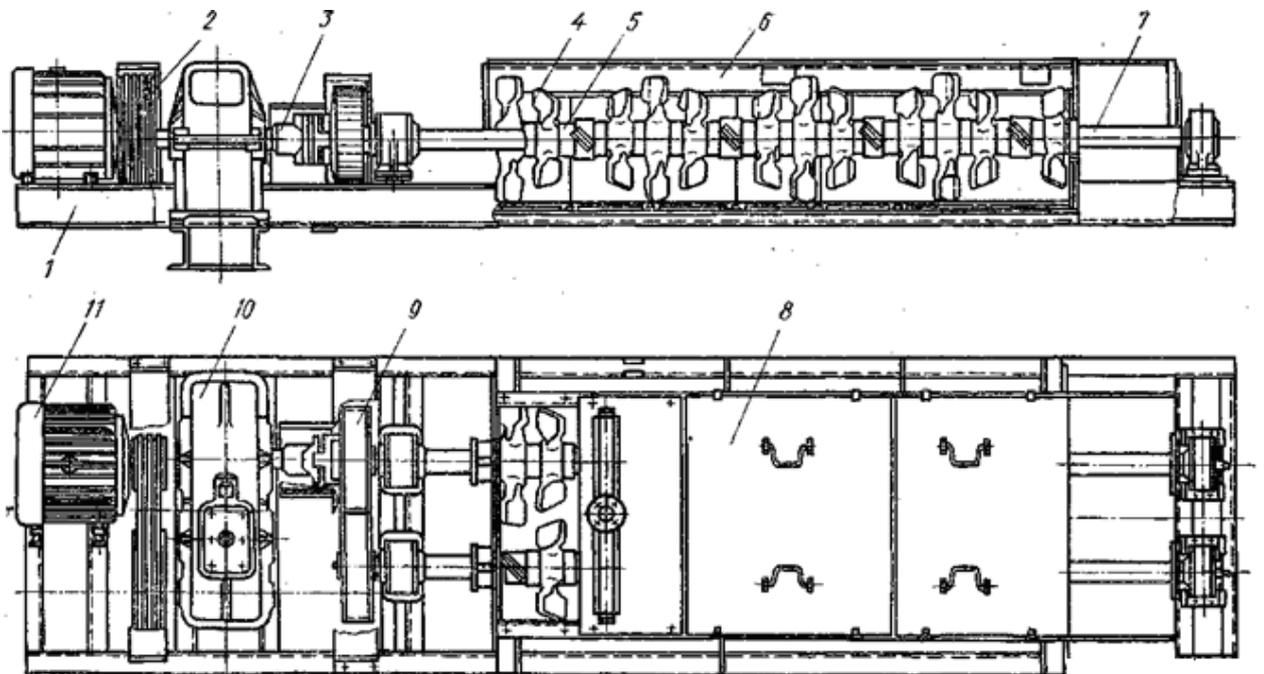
Бетономеситель установки СБ-75: 1 — рама, 2 — клиноременная передача, 3 — муфта, 4 — лопасть, 5 — распорная втулка, 6 — корпус смесителя, 7 — вал, 8 — крышка, 9 — шестерня, 10 — редуктор, 11 — электродвигатель
